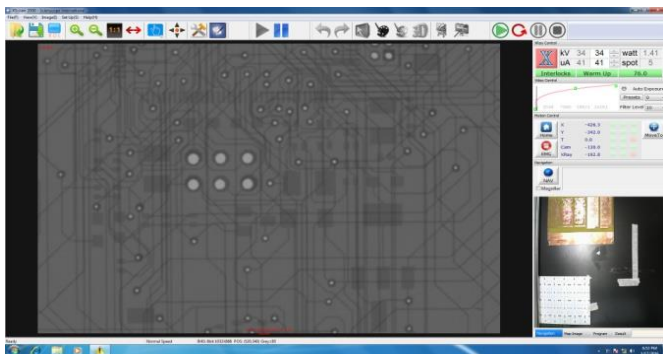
PCB empat layer desain EEG Bottom Layer
